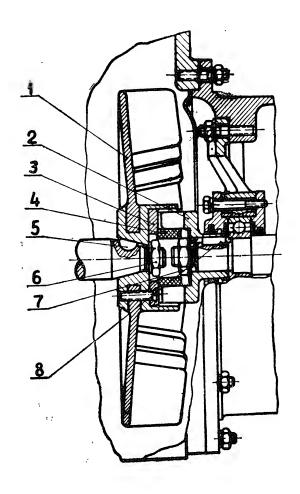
Узел сочленения генератора с двигателем: 1 — вентилятор; 2 — полумуфта вала генератора; 3 — полумуфта вала двигателя; 4 — резиновая прокладка; 5, 8 — шпонки; 6, 7 — гайки.
